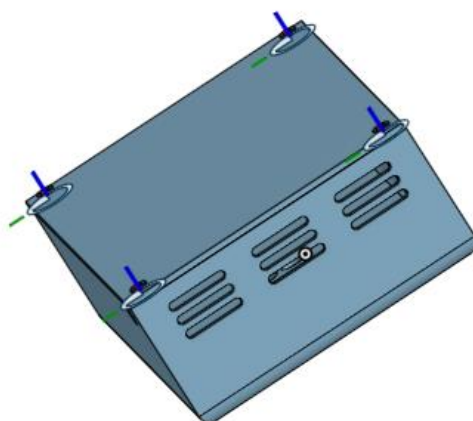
3D-модель збірки елементів корпусу внутрішнього блоку
